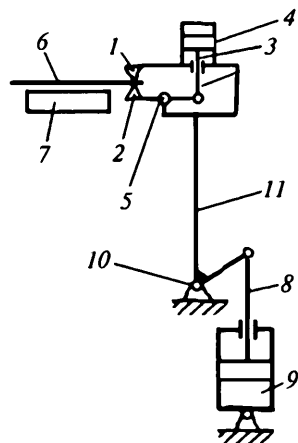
Схема устройства для захвата заготовок, применяемого в установках для механопневмоформования
